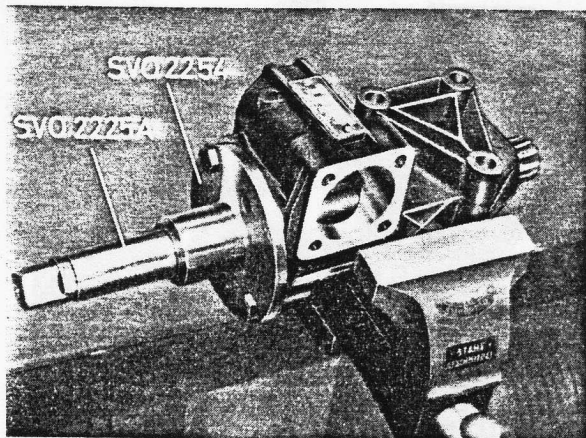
Aufreiben der Buchsen für Lenkrollenwelle
